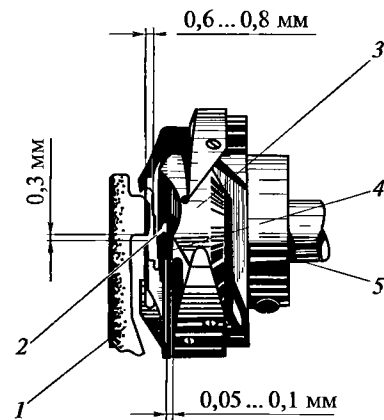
Схема расположения установочного пальца относительно шпуледержателя
